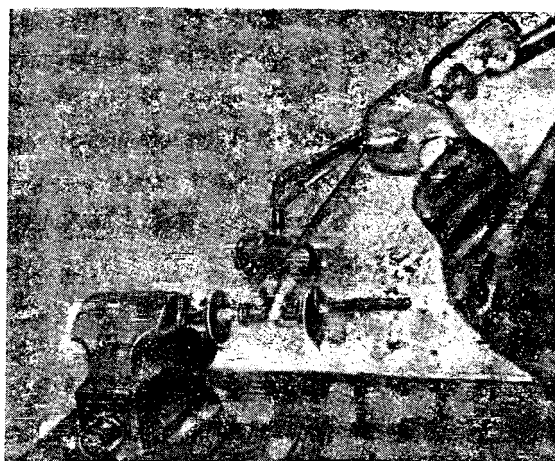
Сварка провода марки АПР с алюминиевыми жилами сечением 95 мм².
